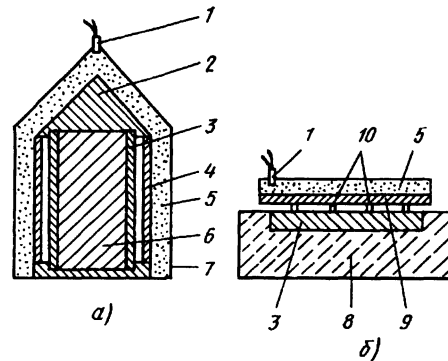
Схемы сборки для сварки взрывом заготовок:
